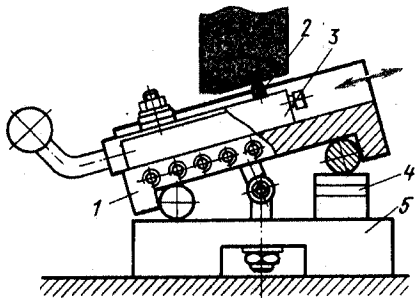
Приспособление для правки прямолинейных участков рабочей поверхности круга
